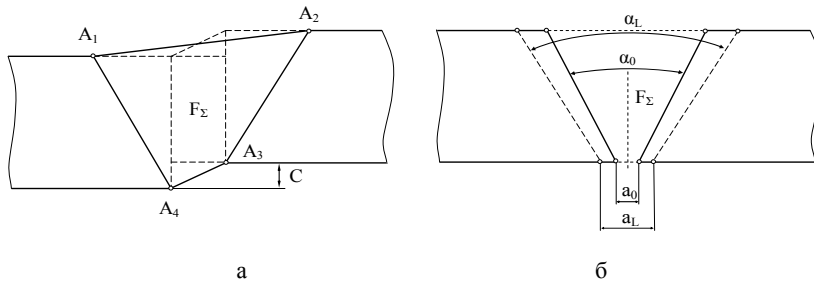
Погрешности сборки стыка под сварку, связанные с образованием:
